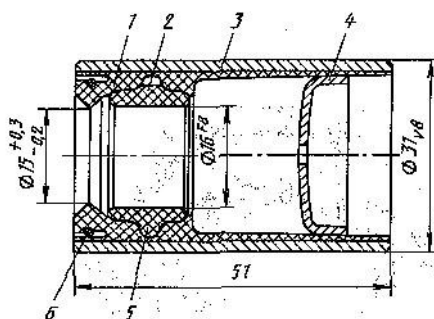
Центрирующая, втулка карданного вала автомобиля «Мерседес 190/190Е». Наружная труба 3 имеет допуск, обеспечивающий надежную посадку во фланце. В трубе имеется эластомерный слой 1, удерживающий втулку 2 из сополимера ацетата с точным внутренним отверстием. Периферийный выступ 5 с сегментными вырезами практически обеспечивает отсутствие радиального перемещения деталей 3 и 2, т. е. отклонения от соосности карданного вала. Проникновение грязи предотвращает запрессованная крышка 4 и уплотнительная кромка; пружинка 6 прижимает эту кромку к подвижной детали карданного вала (рисунок фирмы «Фройденберг»)
